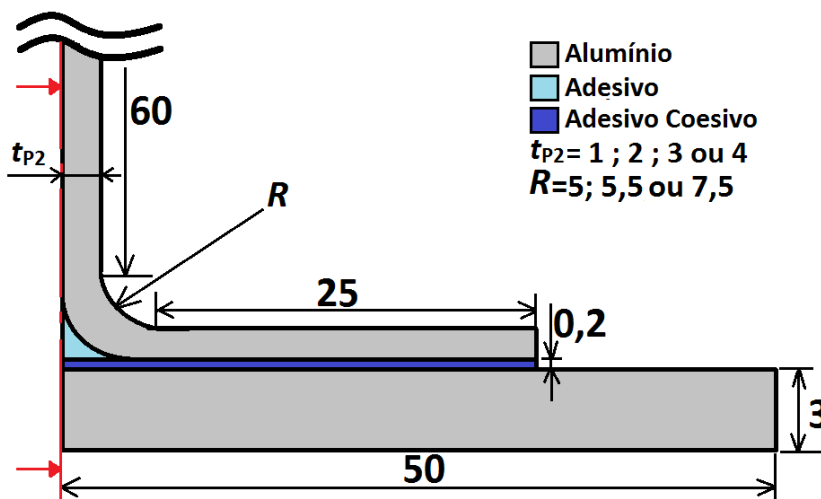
Esquema do modelo da junta em T com adesivo de preenchimento.
